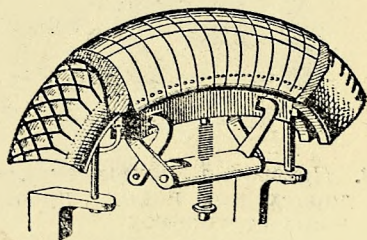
Прессовка покрышки „корсетом“ с одной центральной натяжкой
